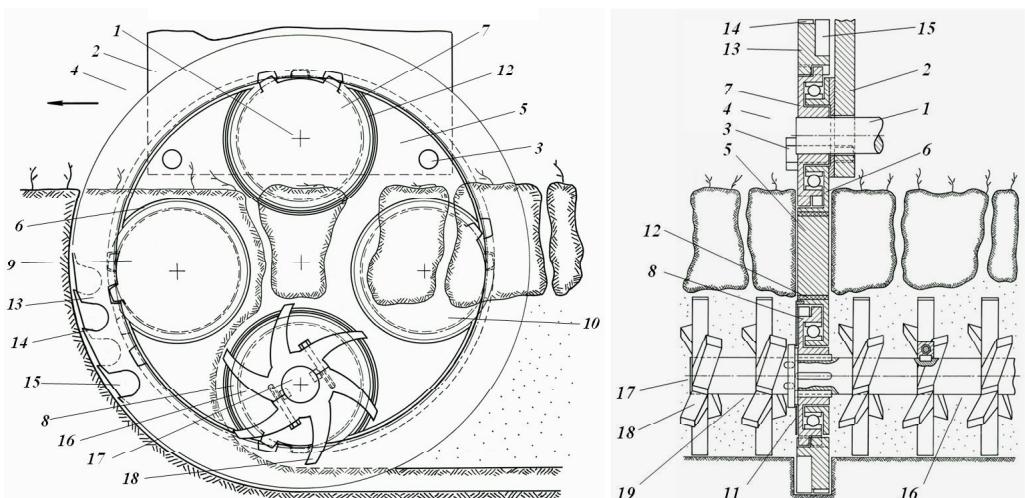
Почвенно-мелиоративное роторное фрезерное устройство с активной редукторной стойкой привода
